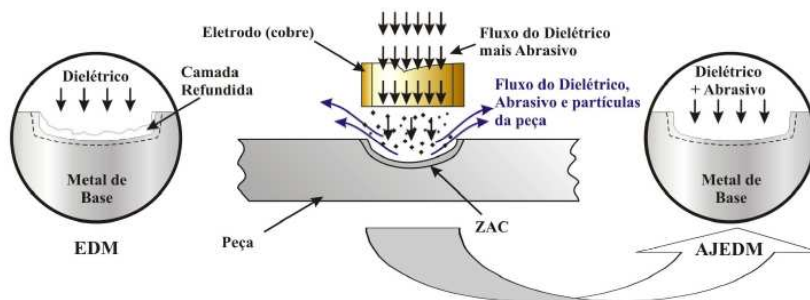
Princípio do processo de usinagem híbrido AJEDM (ARANTES, 2009).
